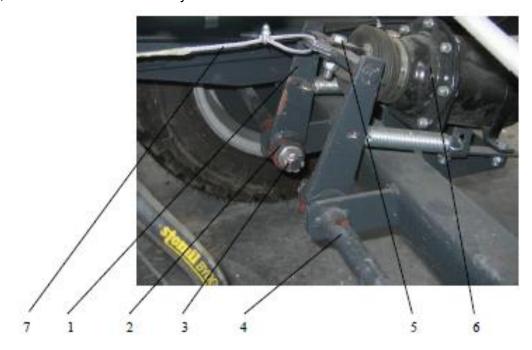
Элементы тормозной системы: 1 - рычаг (плечо) вала расширителя, 2 установочная гребенка, 3 - регулировочный винт для установки рычага (плеча) с гребенкой на валу расширителя, 4 - вал расширителя тормозной колодки, 5 - тяга (толкатель), соединяющая шток пневматического цилиндра с рычагом расширителя, 6 пневматический цилиндр, 7 - трос стояночного тормоза
